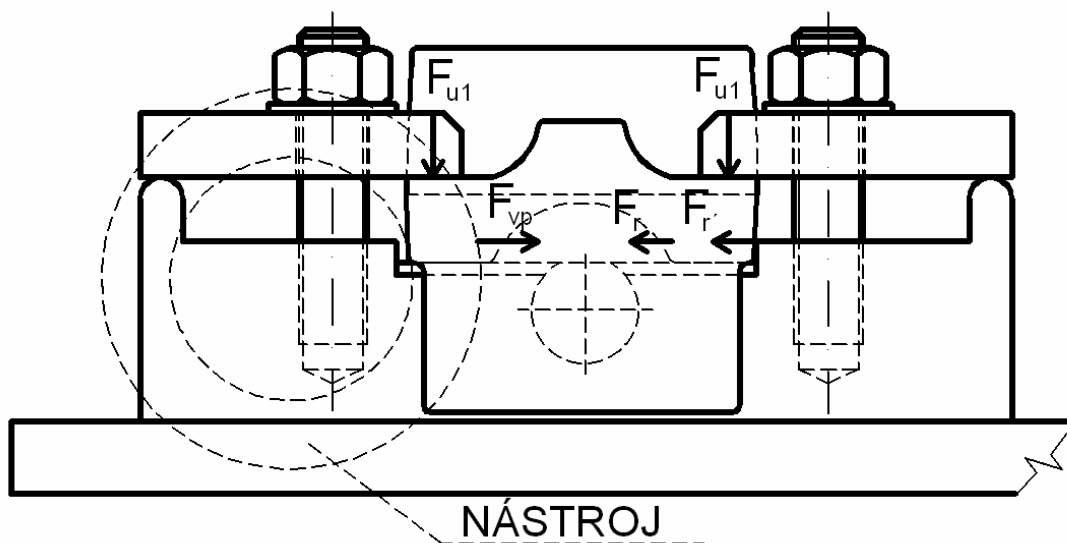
Upnutí obrobku pro třetí a šestou operaci
